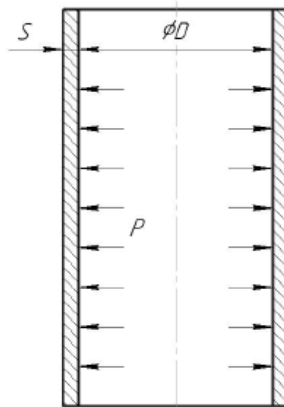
Розрахункова схема для визначення товщини стінки циліндричної обичайки
